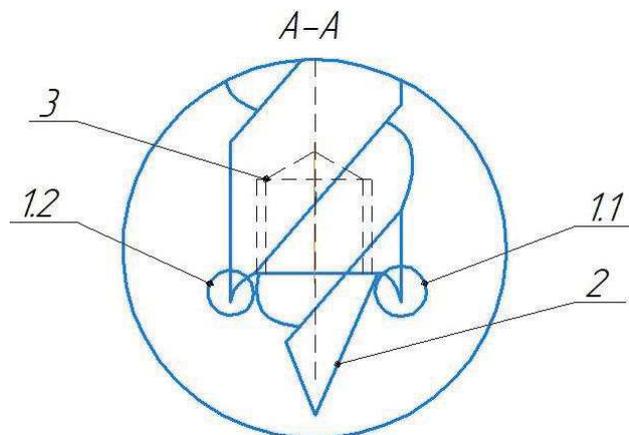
Сборная режущая часть Вид А рисунка 3б
